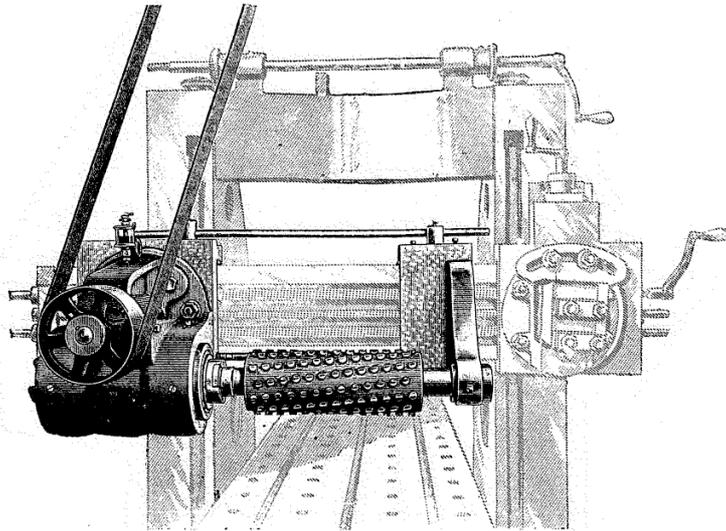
Fraisage auxiliaire raboteuse *Adams*. Application d'une fraise à boutons pour dressage.
